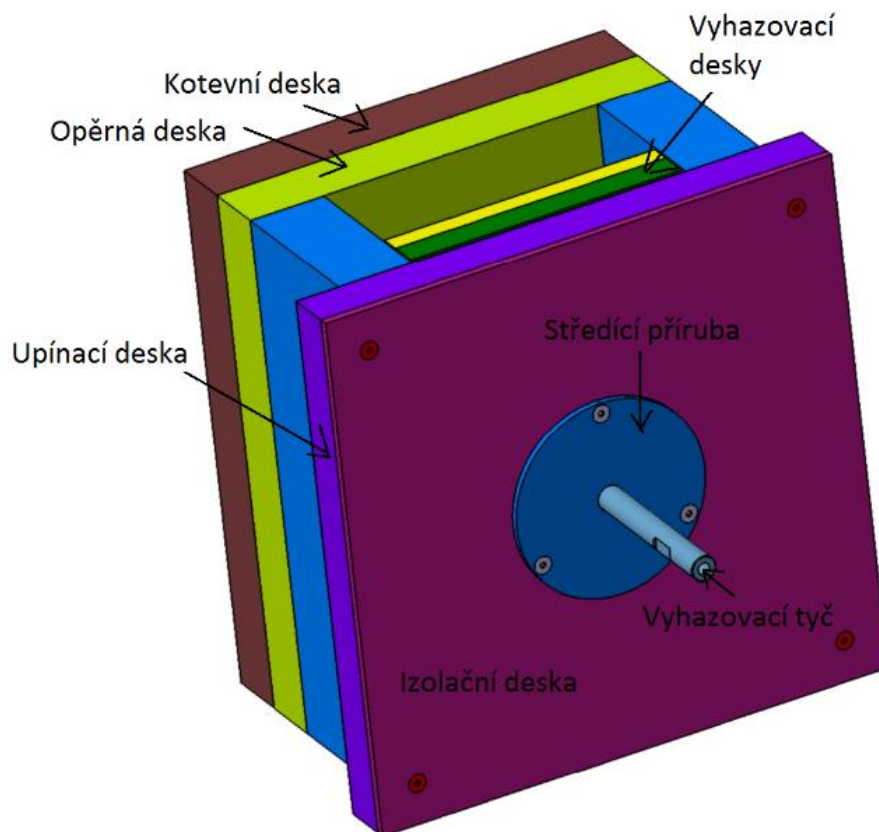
Pravá strana- izometrický pohled - zevnitř
